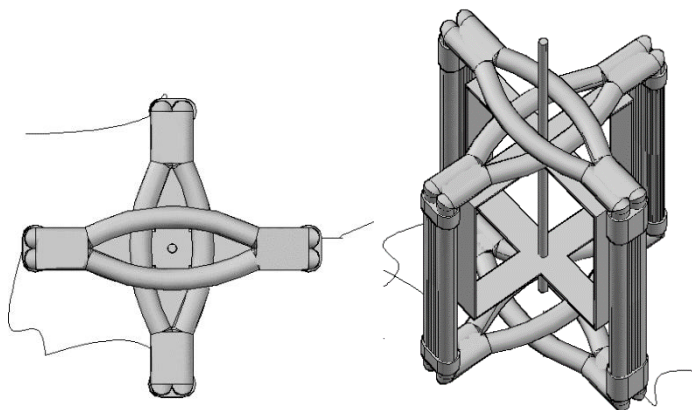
Armado de las bobinas y rotor. Vista superior y en perspectiva.
